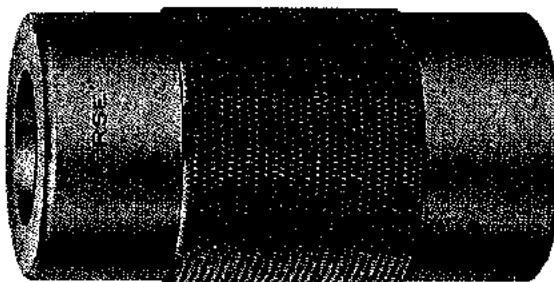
Calibre cónico de anillo (Morse Twist Drill & Machine Co.)
